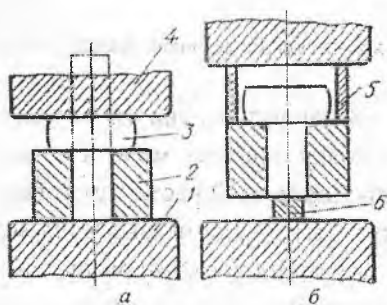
Схемы высадки (а) и удаления заготовки (б): 1 - нижний боек, 2 - кольцо, 3 - заготовка, 4 - верхний боек, 5 - съемное кольцо, 6 - подкладка
